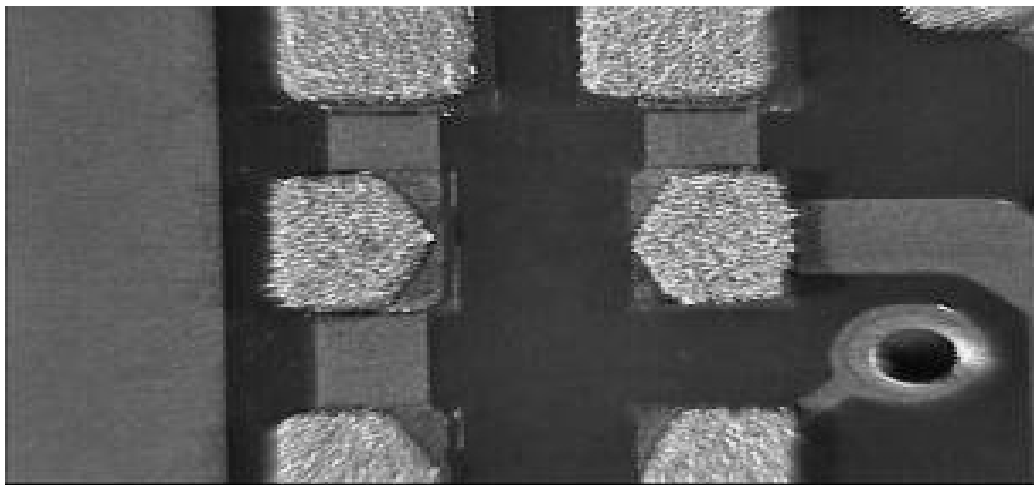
Aplicação de solda em pasta [JUSTI 2006]
